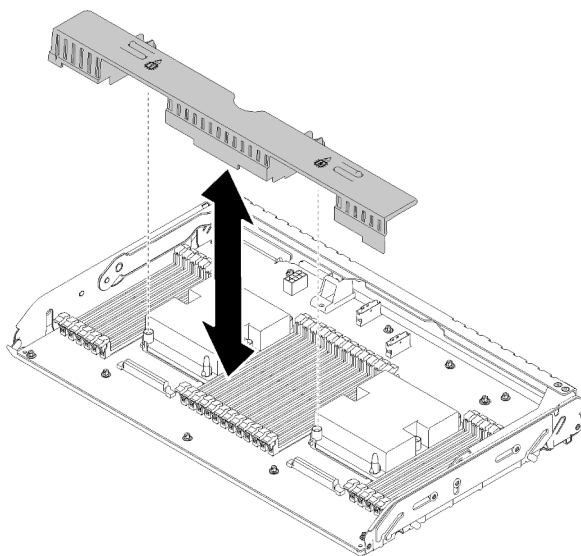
Installation du Grille d'aération de la carte d'extension du processeur et de la mémoire
